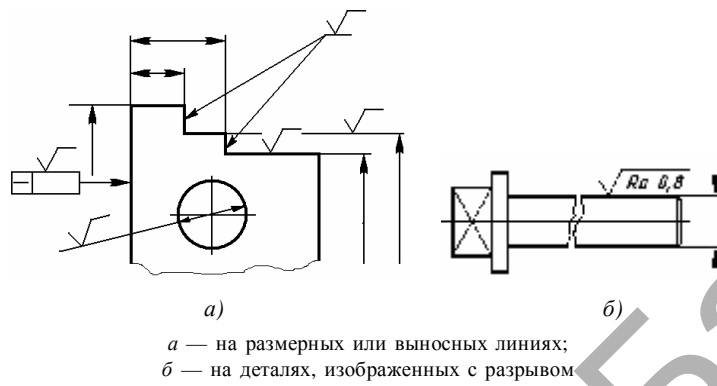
Примеры обозначения шероховатости поверхностей
